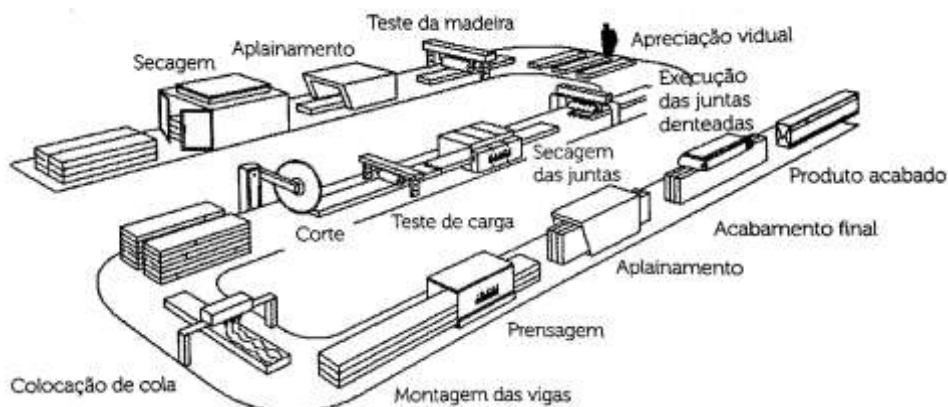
Produção de MLC. Autor Paulo Barreto Cachim
